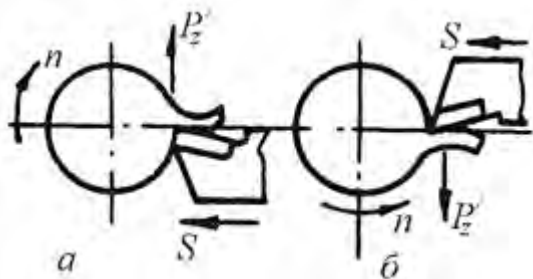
Відрізування заготовок при прямому (а) і зворотному (б) обертанні шпинделя
